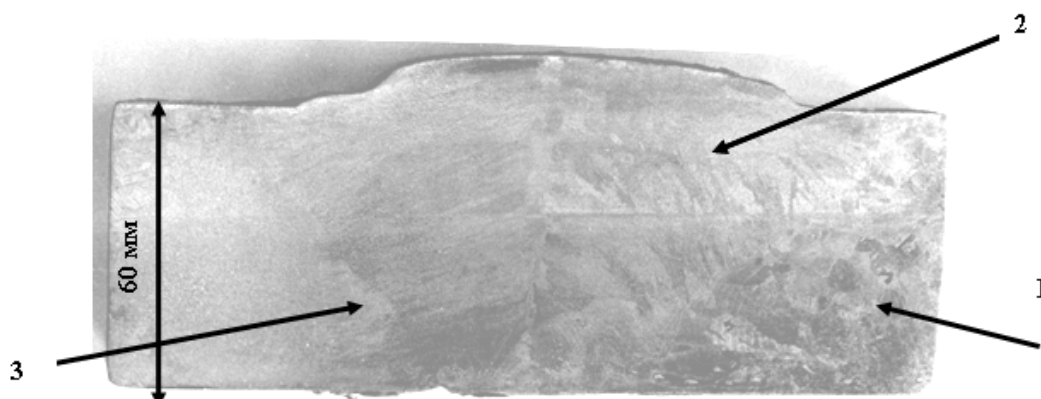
Макрошлиф сварного соединения меди М1р толщиной 60 мм, полученного однопроходной сваркой плавлением: 1 – основной металл; 2 – металл шва; 3 – зона сплавления
